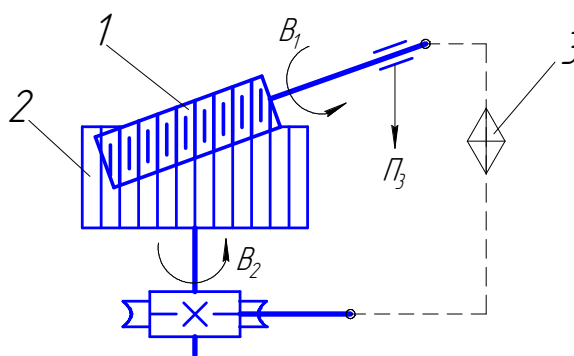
Станочное зацепление червячная фреза – заготовка
